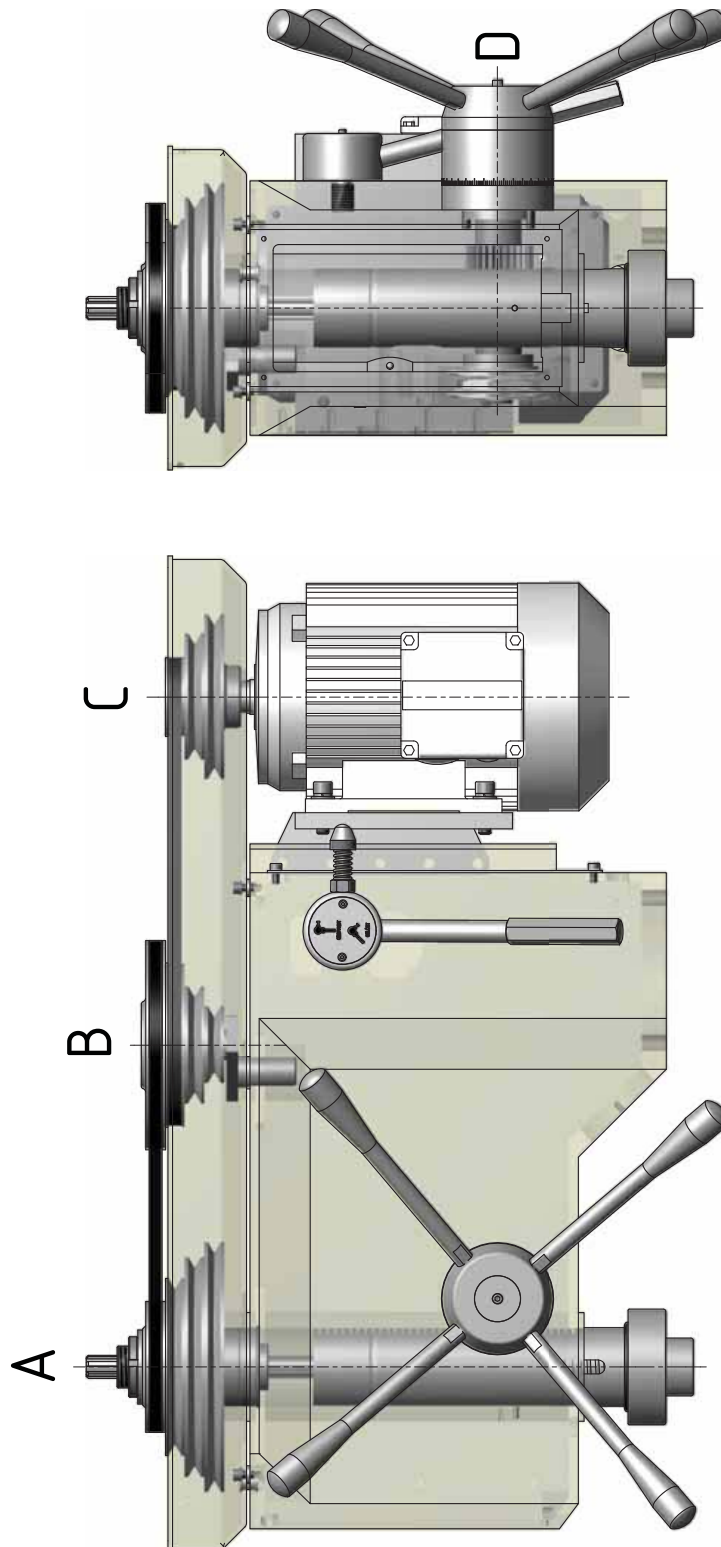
Bohrkopf B34H - Drilling head B34H
